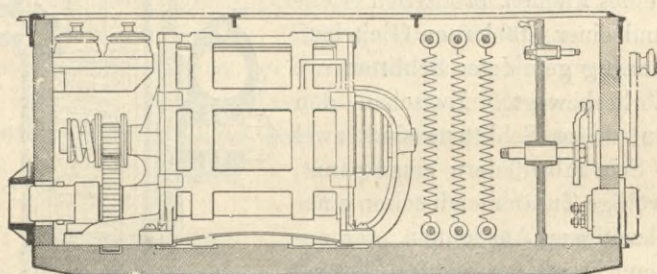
Motorkasten mit eingebautem Drehstrommotor.
